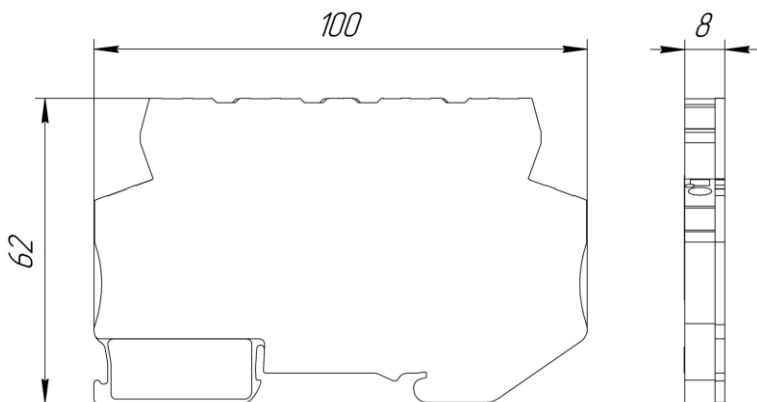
Габаритный чертеж модулей NLS-1R12, NLS-1R24 с боковой крышкой
